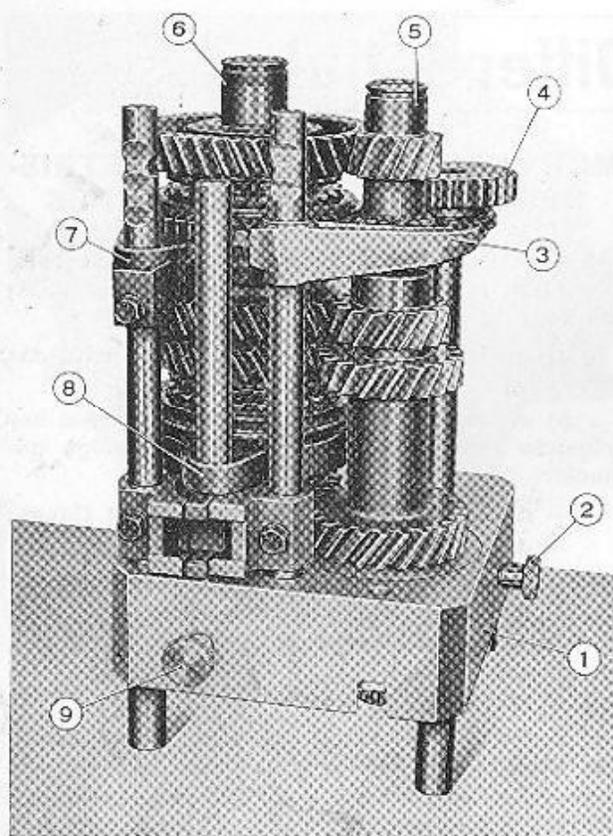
Vorläufige Montage des Getriebes auf dem Werkzeug A. 70105.
